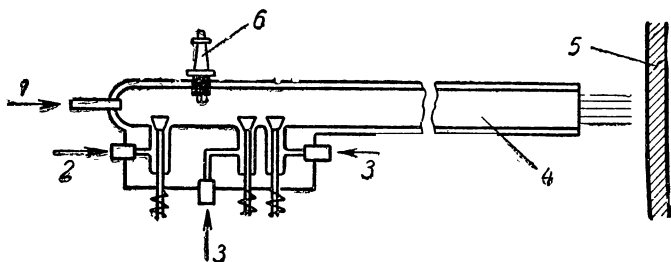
Напыление взрывом: 1 — порошок; 2 и 3 — штуцеры; 4 — смесительная камера; 5 — обрабатываемая деталь; 6 — воспламенитель.
